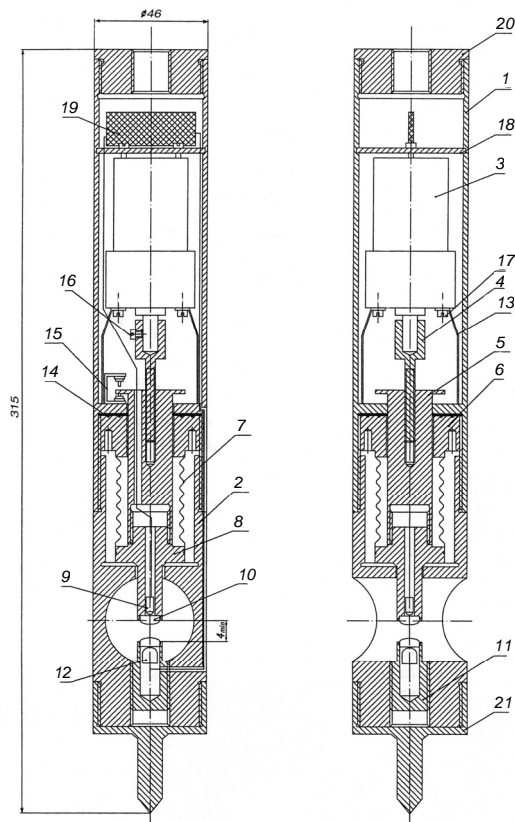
Чертеж общего вида турбидиметра с переменной измерительной базой: 1 — основание корпуса; 2 — рабочая часть корпуса; 3 — электродвигатель с редуктором; 4 — приводная насадка; 5 — скользящий управляемый толкатель; 6 — основание сильфонного узла; 7 — сильфон; 8 — держатель фотодиода; 9 — фотодиод; 10 — линза; 11 — держатель светодиода; 12 — светодиод; 13 — стойка-упор; 14 — прокладка; 15 — узел концевых выключателей; 16 — винт М3; 17 — винт М4; 18 — пластина-упор; 19 — плата преобразователя; 20 — переходник для подводящей трубки $\varnothing 16$; 21 — подпирющий наконечник
